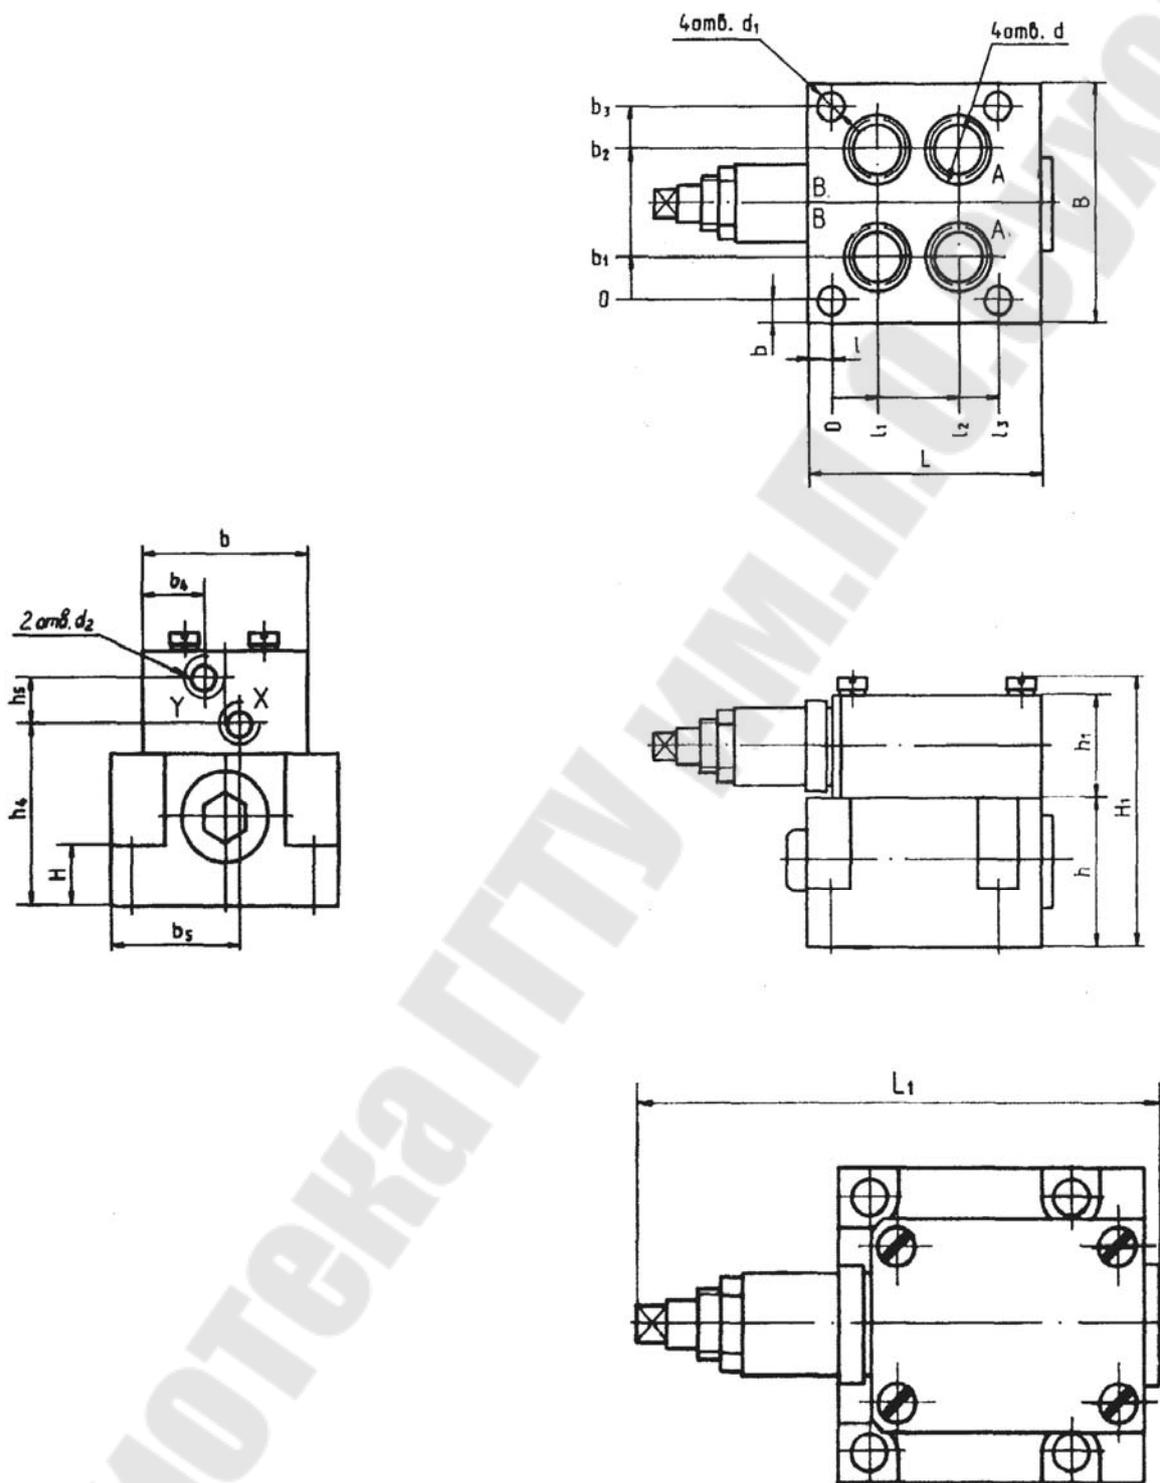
Общий вид блока присоединительного клапана редукционного БВП-6КР
